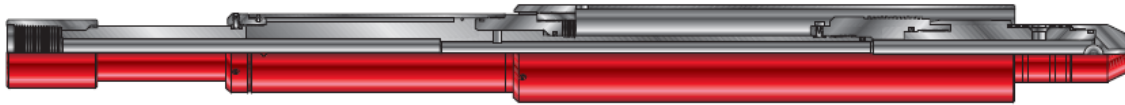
Hydraulic Setting Tool. Tomado de “Model AH Hydraulic Setting Tool”. Tomado de www.weatherford.rio.com.br
